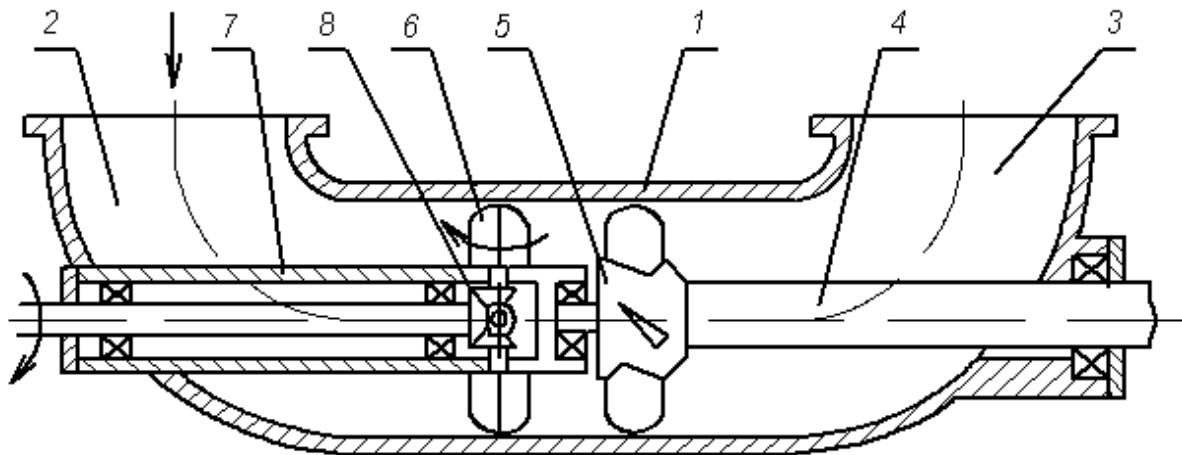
Кавітаційний змішувач з механізмом регулювання кута атаки: 1 – корпус; 2 – патрубок подачі вихідної суміші; 3 – патрубок відведення; 4 – вал; 5 – кавітаційний елемент; 6 – крильчатка; 7 – втулка; 8 – механізм повороту лопатей
